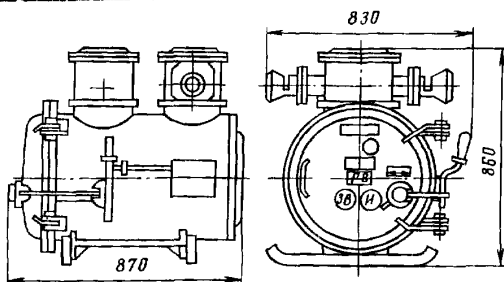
Габаритные размеры пускателя ПВИ-250БТ
